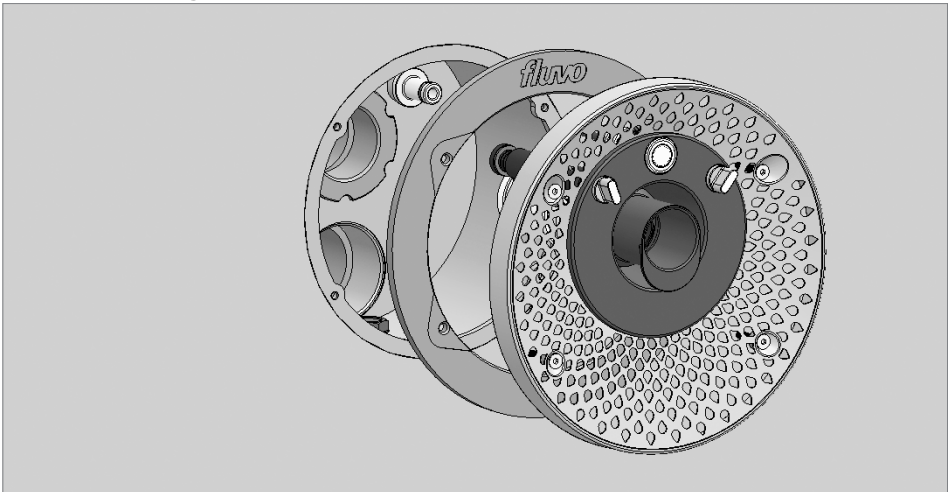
Düsenkopf einstecken und anschrauben (Edelstahlausführung mit Fliesen- bzw. Abstandsring abgebildet)
